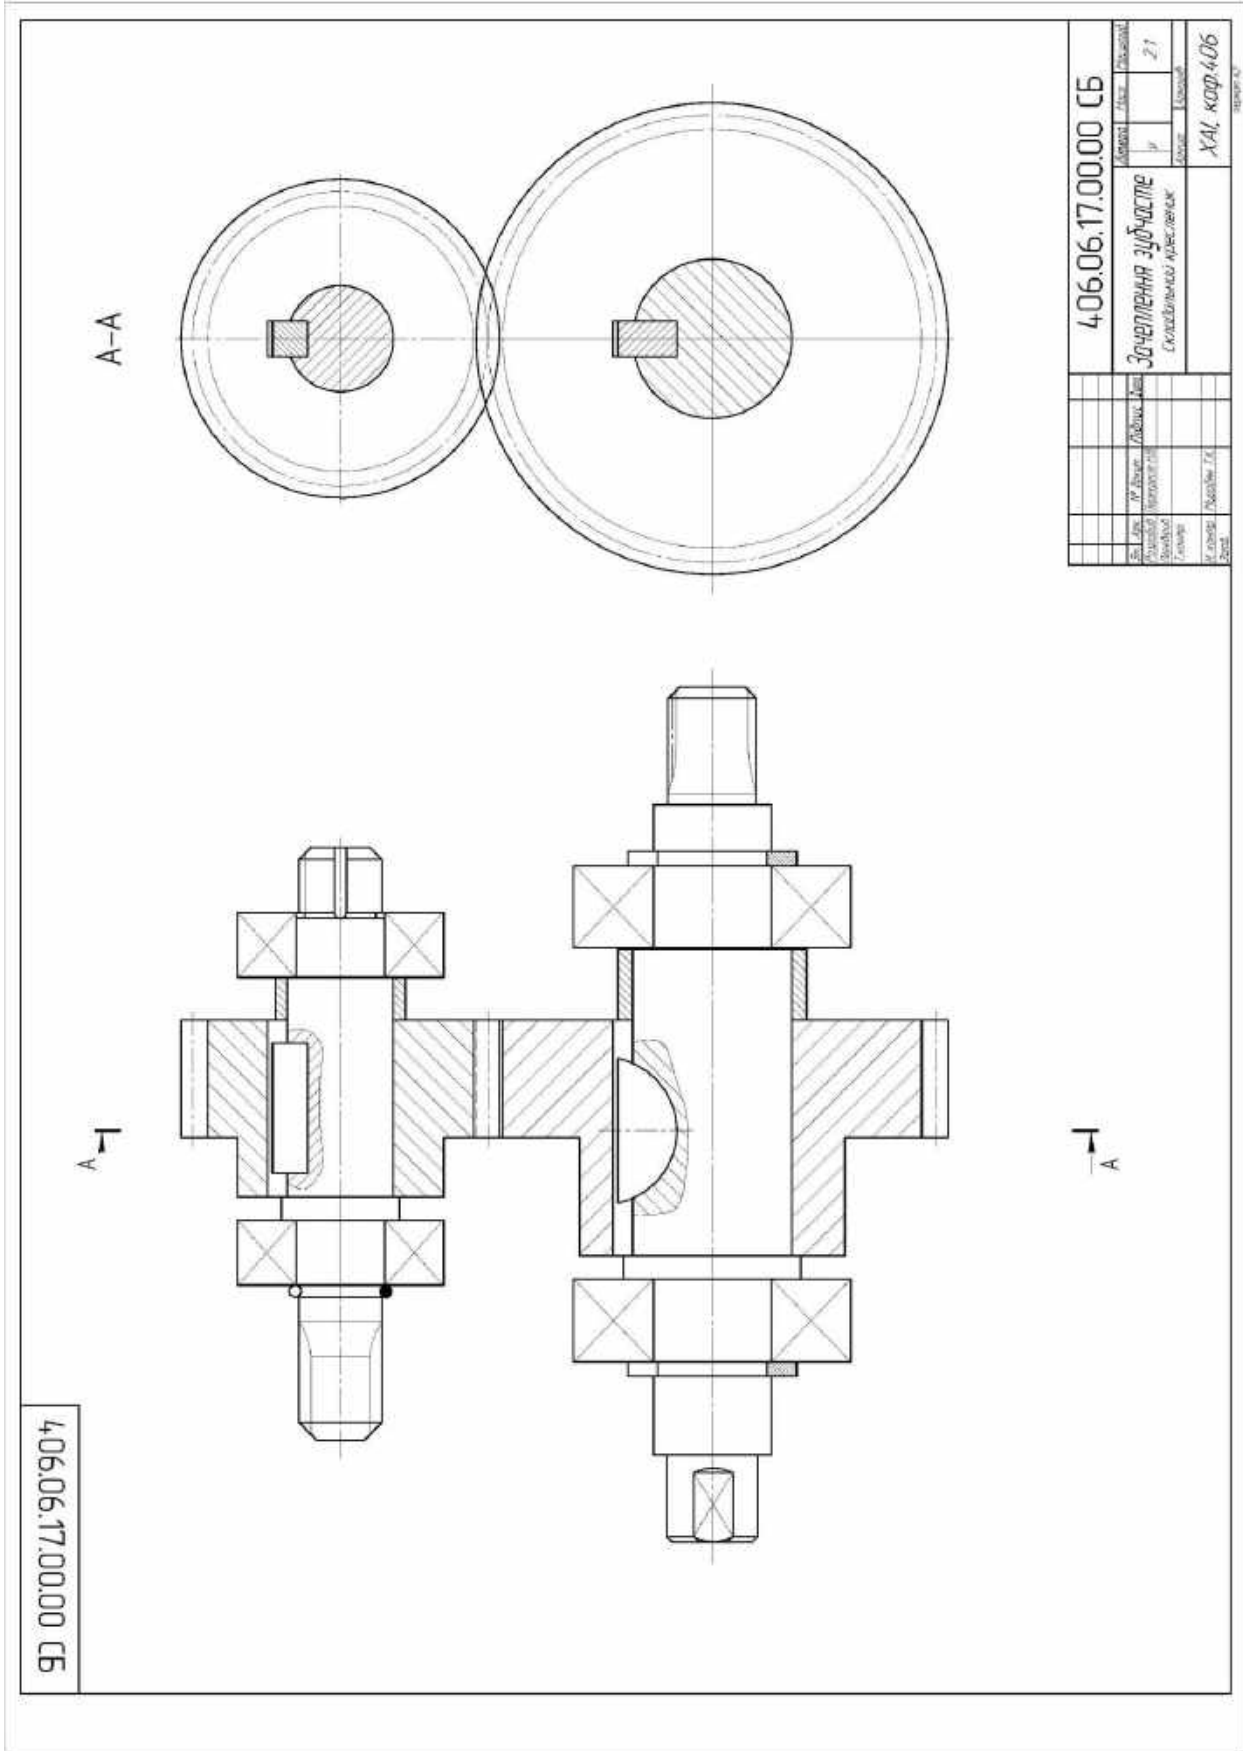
П'ятий етап виконання складального креслення зубчастого зачеплення із підшипниками
